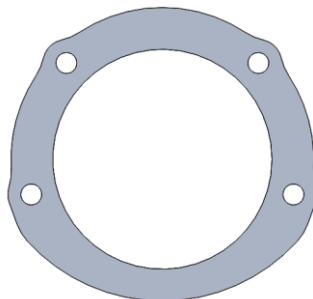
Vistas frontal de la pieza asiento de rodamiento
